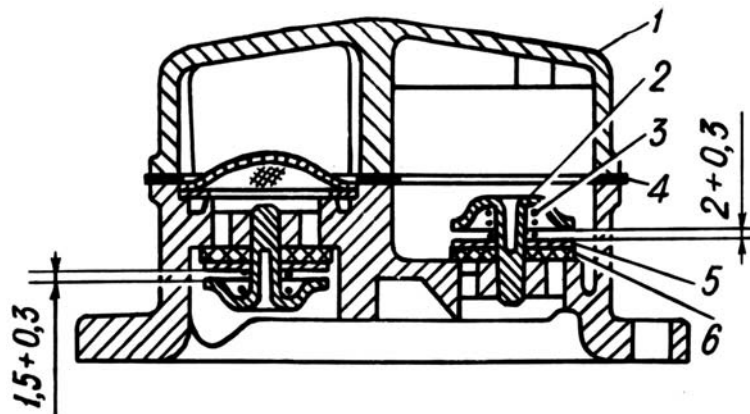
Головка топливного насоса: 1 - крышка; 2 - обойма клапана; 3 - пружина; 4 - прикладка; 5 - пластина клапана; 6 - клапан
